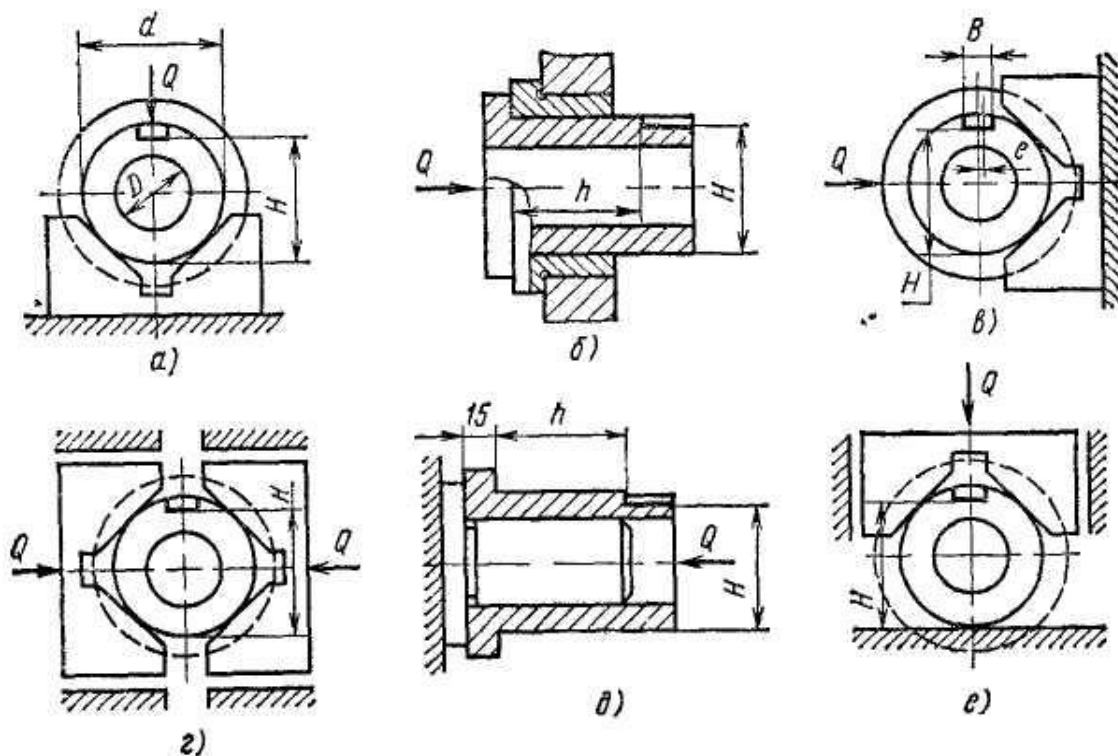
Схема установки заготовки при обробці шпоночного пазу
